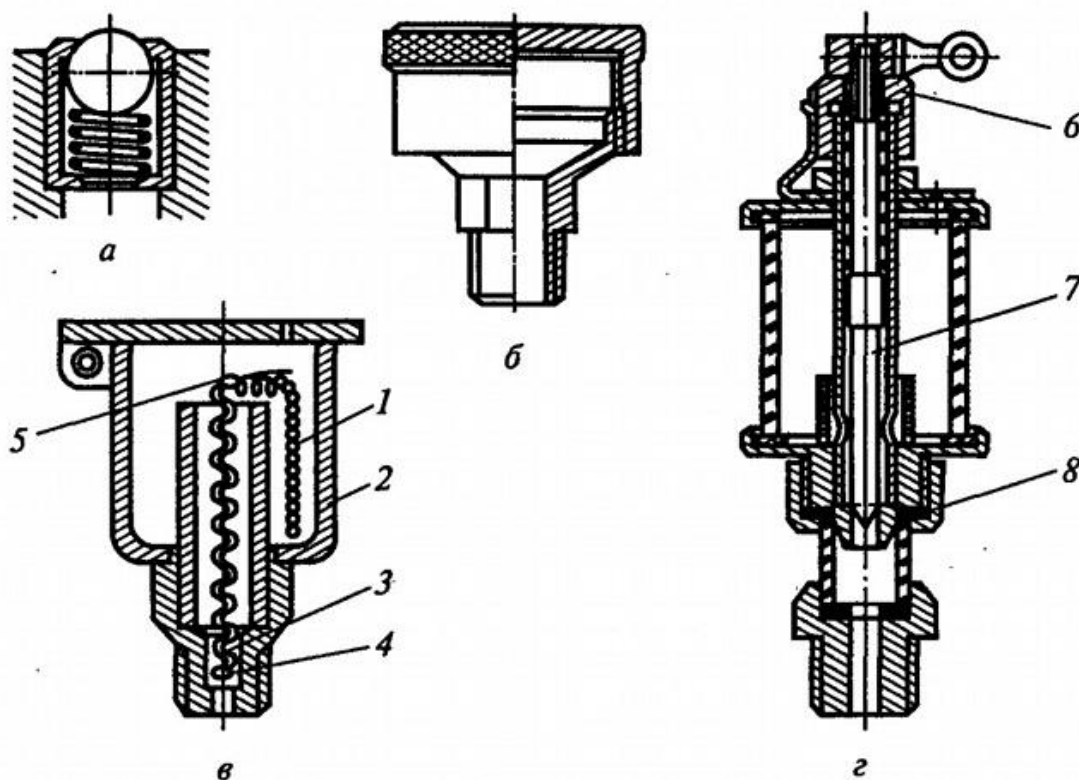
Масленки индивидуального смазывания: а — с шариковым клапаном; б — колпачковая; в — фитильная; г — капельная; 1 — фитиль; 2 — резервуар; 3 — канал; 4 — петля; 5 — усики; 6 — гайка; 7 — игла; 8 — отверстие
